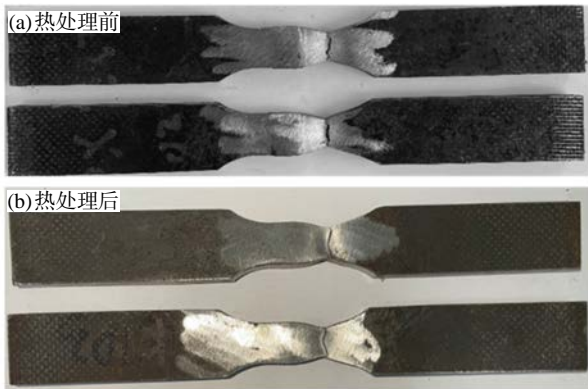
K-TIG 焊接接头拉伸试样形貌
